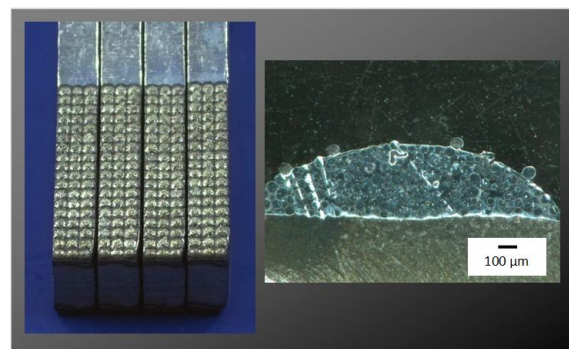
Punktrasterfläche (links), Querschliffbild eines einzelnen Schweißpunktes (rechts)
